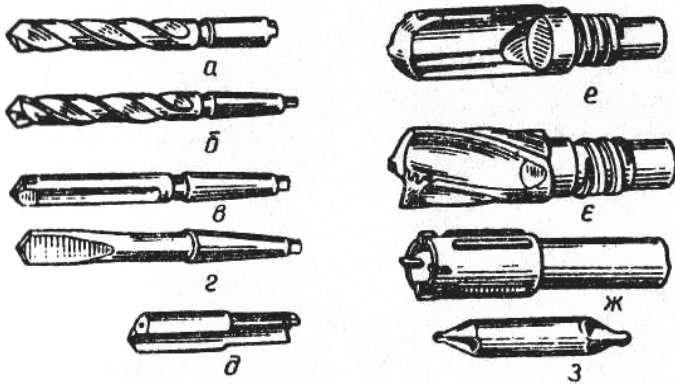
Свердла: а, б – спіральні; в – з прямими канавками; г – перове; д – спеціальне; е – однокромочне з внутрішнім відведенням стружки для глибокого свердління; є – двокромочне для глибокого свердління; ж – для кільцевого свердління; з – центровочне
